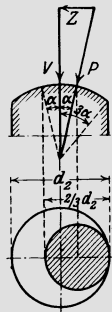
Bew.-Widerstände am unteren Zapfen.
